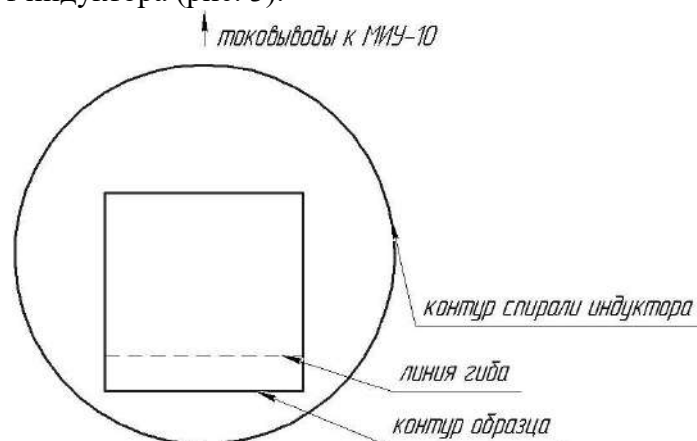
Схема установки квадратных образцов под круглым индуктором
